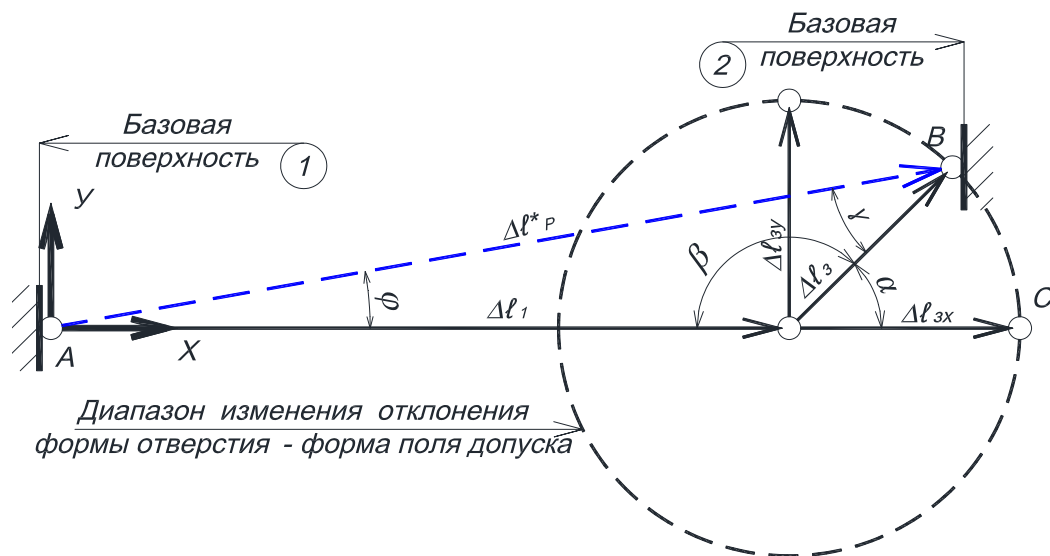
Модель размерной цепи, учитывающая положение и форму отверстий
